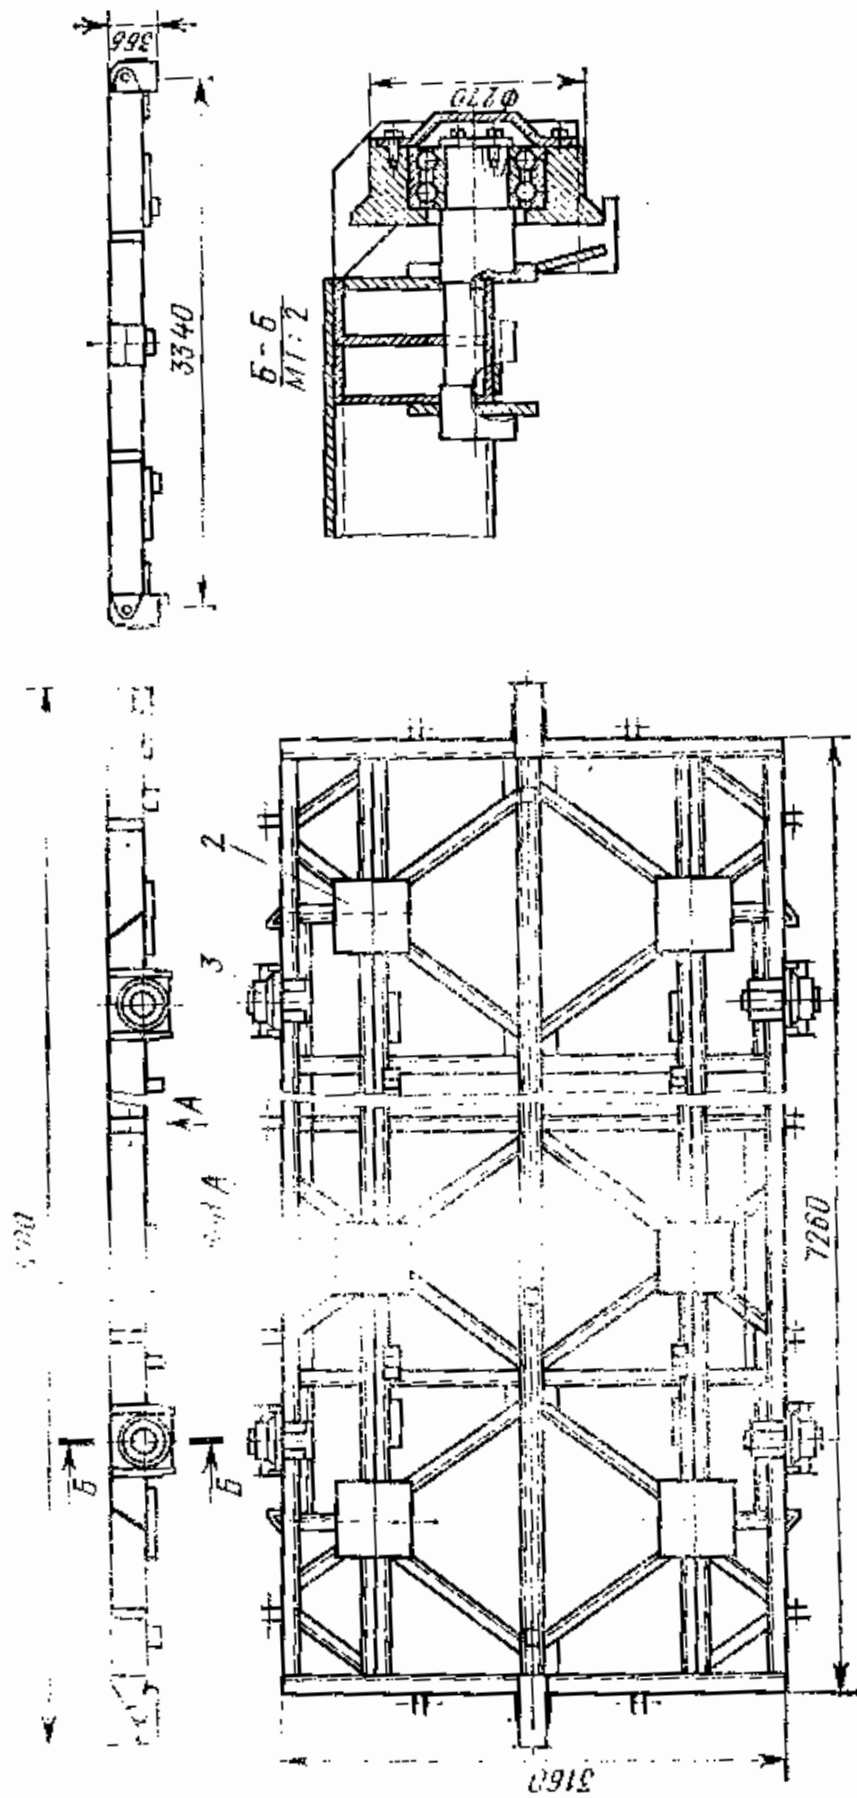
Поддон СМЖ-3010Б для изготовления плоских железобетонных изделий:
